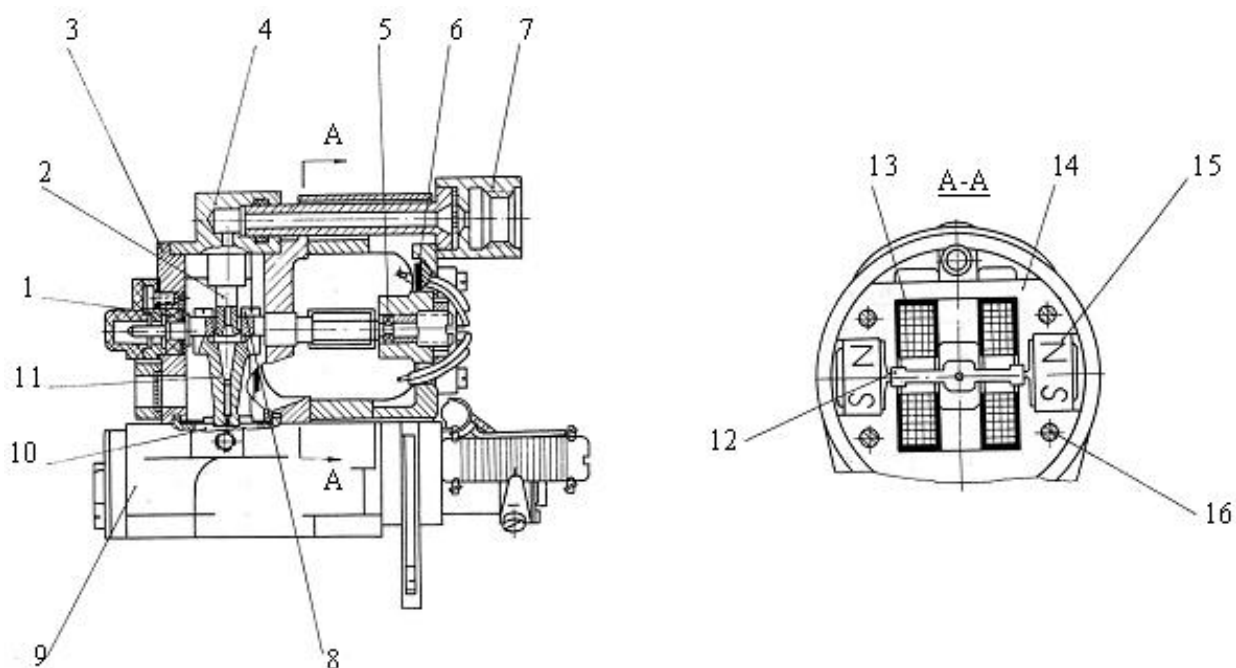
Конструкция газового распределителя: 1,5 – подшипники; 2 – ниппель; 3 – корпус; 4,6 – фланцы; 7 – кронштейн; 8 – винт; 9 – кронштейн; 10 – приемная часть; 11 – сопло; 12 – якорь; 13 – катушка; 14 – магнитопровод; 15 – постоянный магнит; 16 – шпилька
